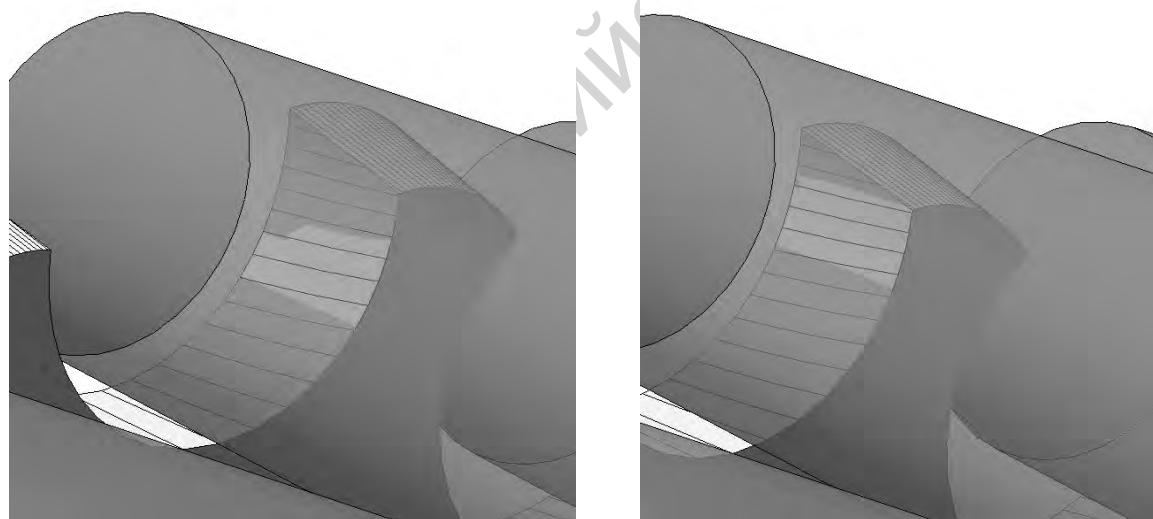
Пятно контакта в прецессионной роликовой передаче с переходной зубчатой поверхностью сателлитного колеса
